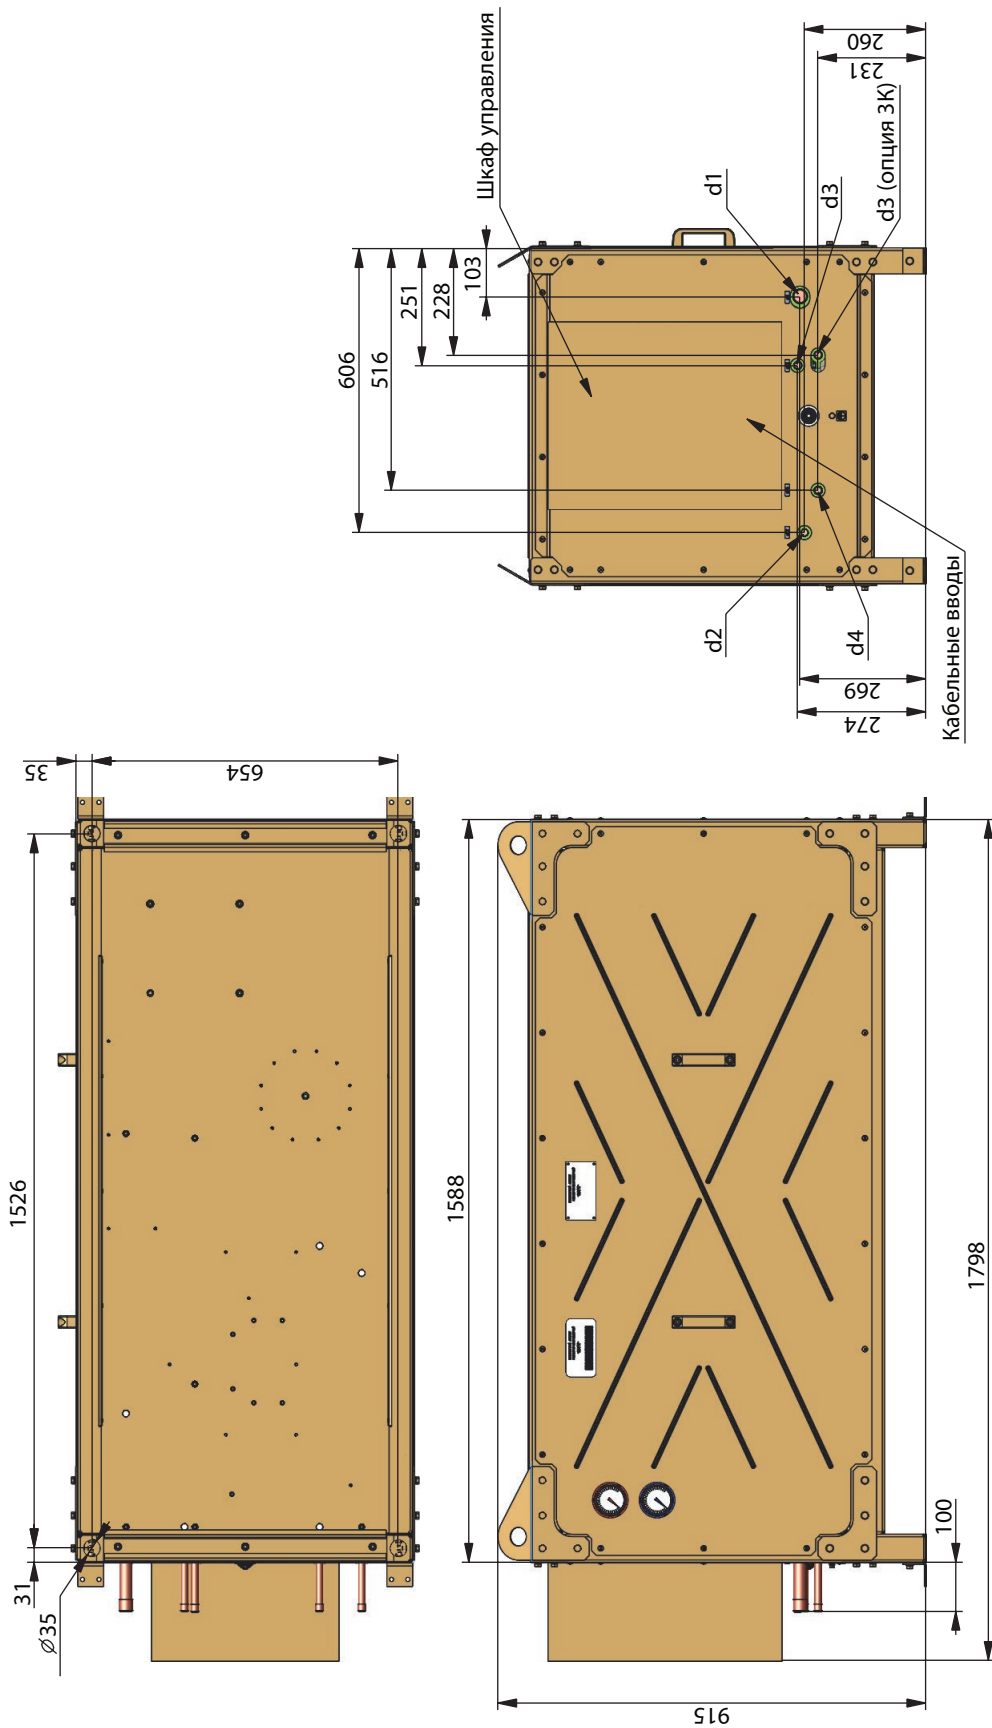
Агрегат компрессорный типа МАРК 100-151, -201
